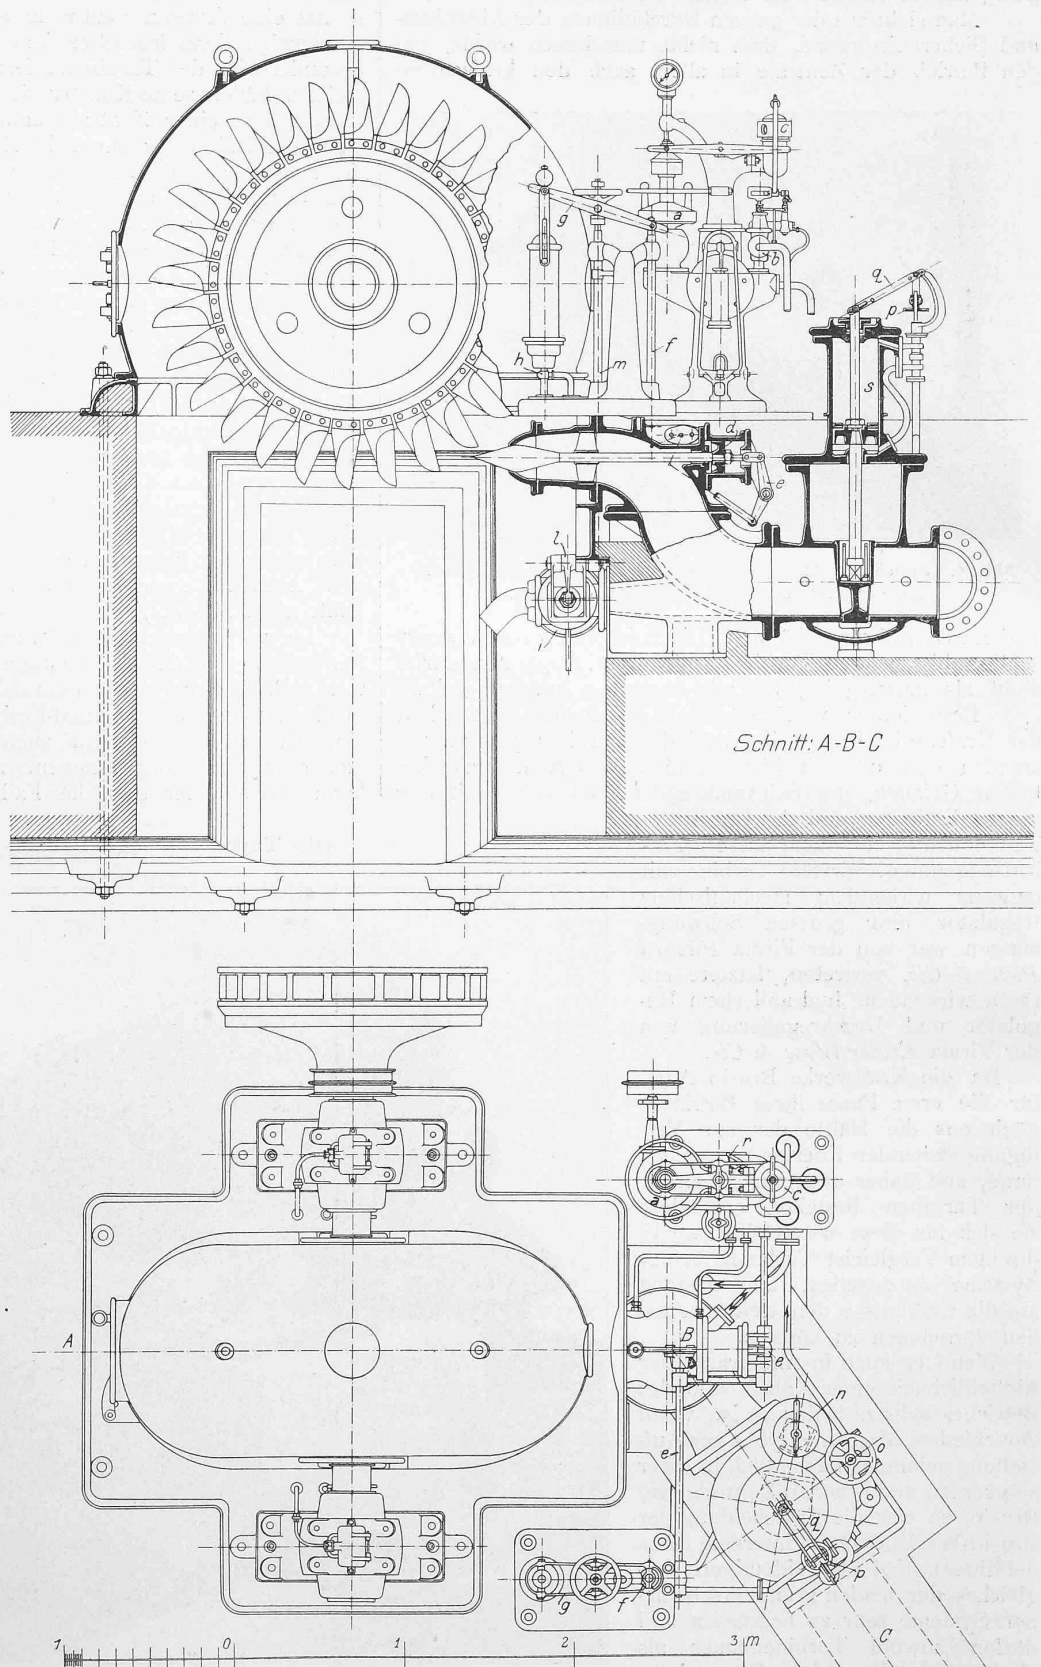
und 7. Vertikalschnitt A-B-C, Teil-Ansicht und Grundriss der 3500 PS-Turbine samt Regulierung. — Masstab 1:40.
